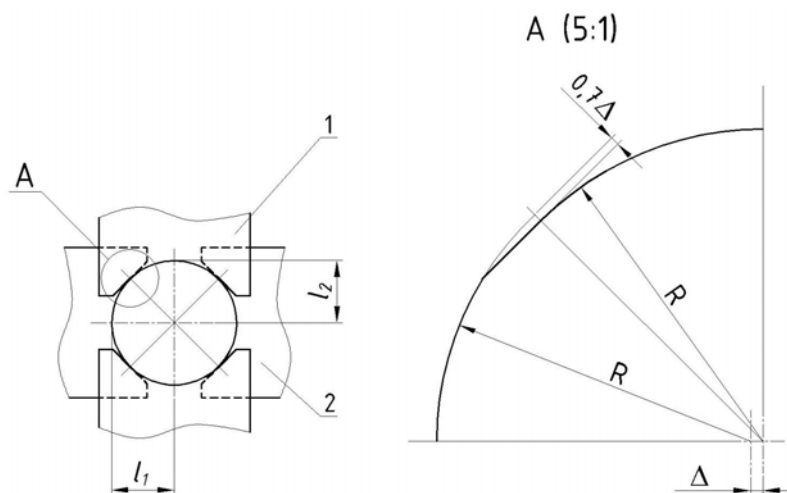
Схема формирования поперечного сечения цилиндрической детали при участии четырех фрез
